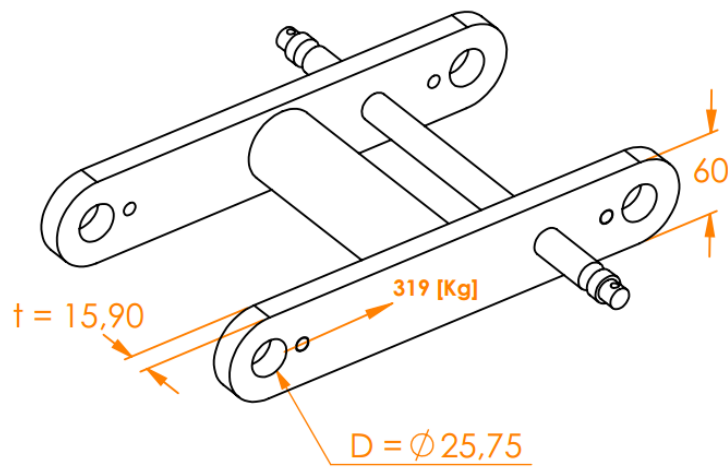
compresión local o aplastamiento laterales parrillas. Elaboración propia.
